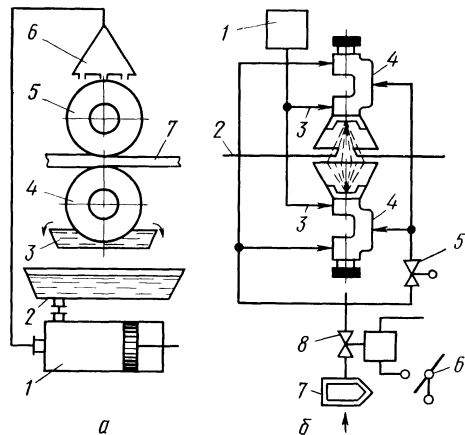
Подача смазки на полосу перед листовой штамповкой и вырубкой (а — контактная, б — обрызгиванием) [434]
